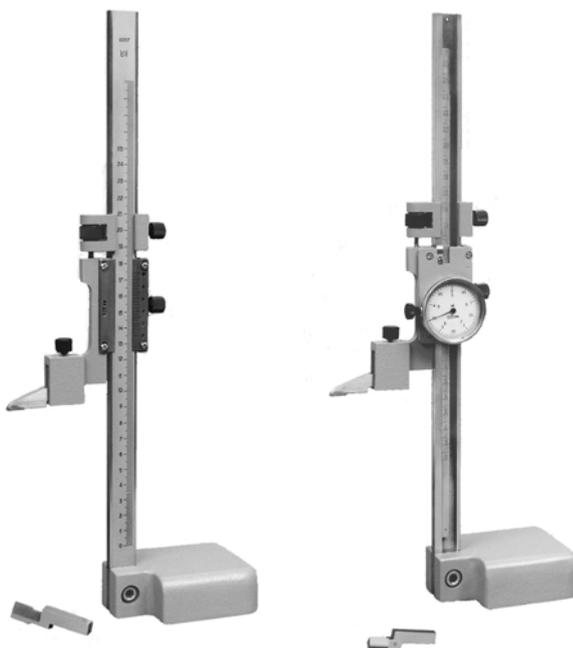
Общий вид штангенрейсмаса ШР, ШРК
